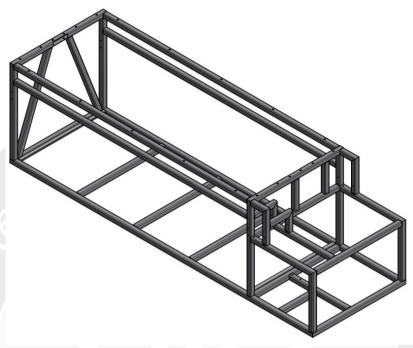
Gambar Dimensi Mesin Pengering Cengkeh
